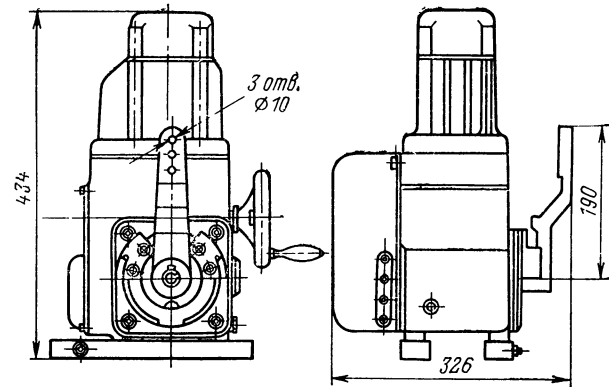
Исполнительный механизм МЭК-10к/120.
